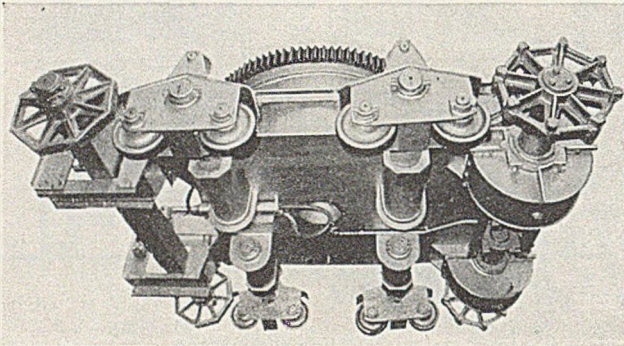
Elektrisch geschweißter Unterwagen mit staub- und wasserdicht eingebautem Raupenfahrtrieb und mit acht in Schwingen gelagerten Laufrädern.
